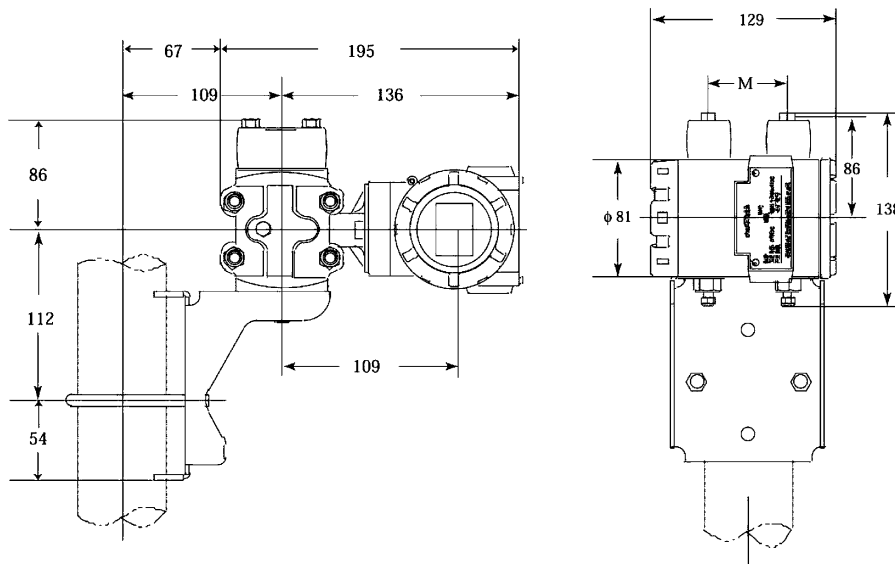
Типовые схемы установки. Крепление на вертикальной панели.
